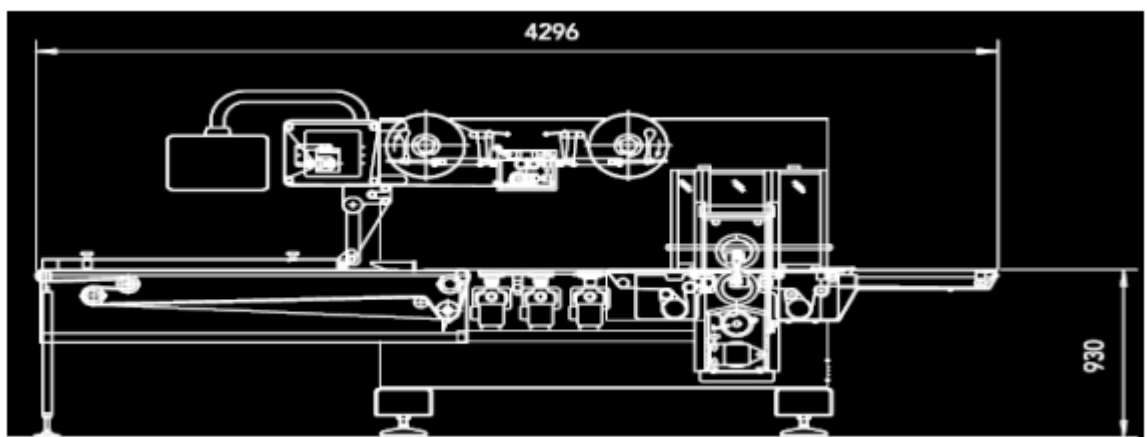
Схематичний вигляд горизонтальної обгорткової машини, версія ВА.
